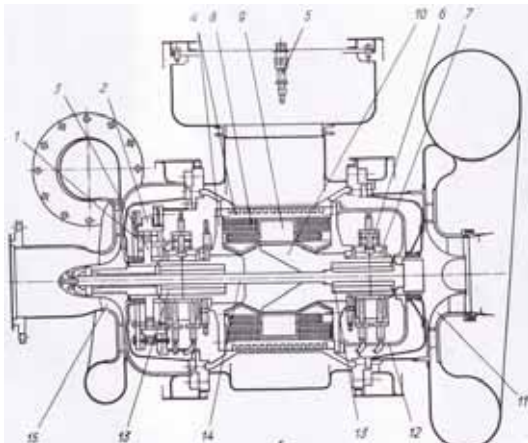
Принципиальная схема турбокомпрессора-генератора мощностью 2-15 кВт: 1-корпус упорного подшипника; 2- карданный подвес упорного подшипника; 3-диск упорного подшипника; 4- корпус и торцевые крышки генератора; 5-разъемы емкостных датчиков; 6- корпус опорного подшипника; 7- сектор опорного подшипника; 8- обмотка возбуждения; 9- пакет железа статора; 10- ротор генератора; 11- колесо турбины; 12- радиационный экран; 13- тепловой мост; 14- стяжной болт; 15- колесо компрессора
